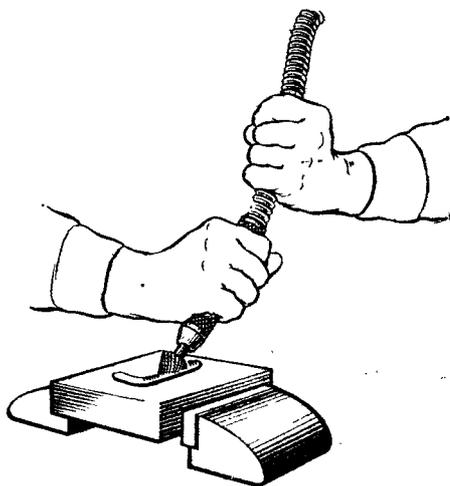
Прием обработки поверхностей фрезами-шарошками
